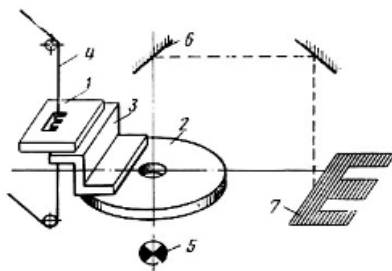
Схема копировально-вырезного станка: 1 – электрод-деталь; 2 – координатный стол; 3 – приспособление для крепления детали; 4 – электрод-проволока; 5 – подсвет; 6 – оптическая система; 7 – копер-экран
